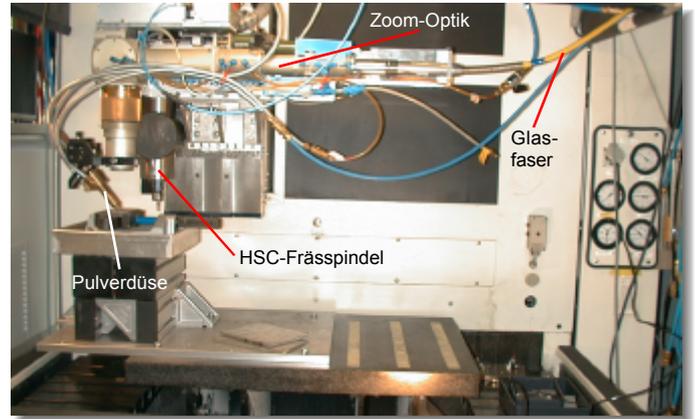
Laserintegrierte HSC-Fräsmaschine zum Rapid Prototyping
